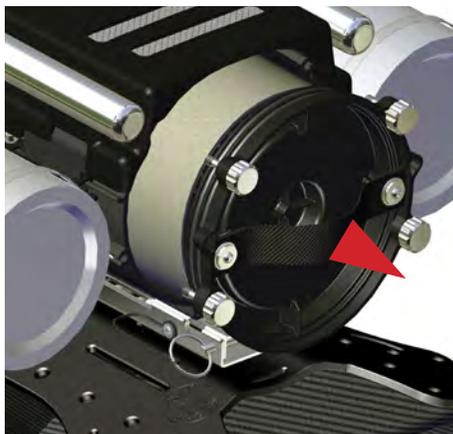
Entfernen Sie die Bodenplatte.
